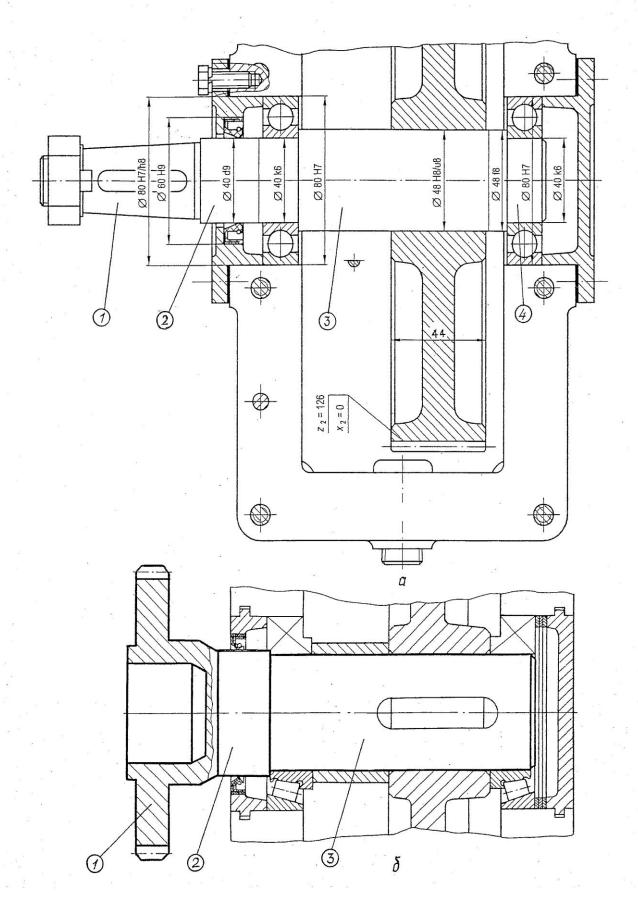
Тихоходный вал редуктора с одним насадным цилиндрическим зубчатым колесом тихоходной ступени: с коническим концом (а) и концом в виде части зубчатой муфты (б) (к примерам соответственно 2.13 и 2.14)
